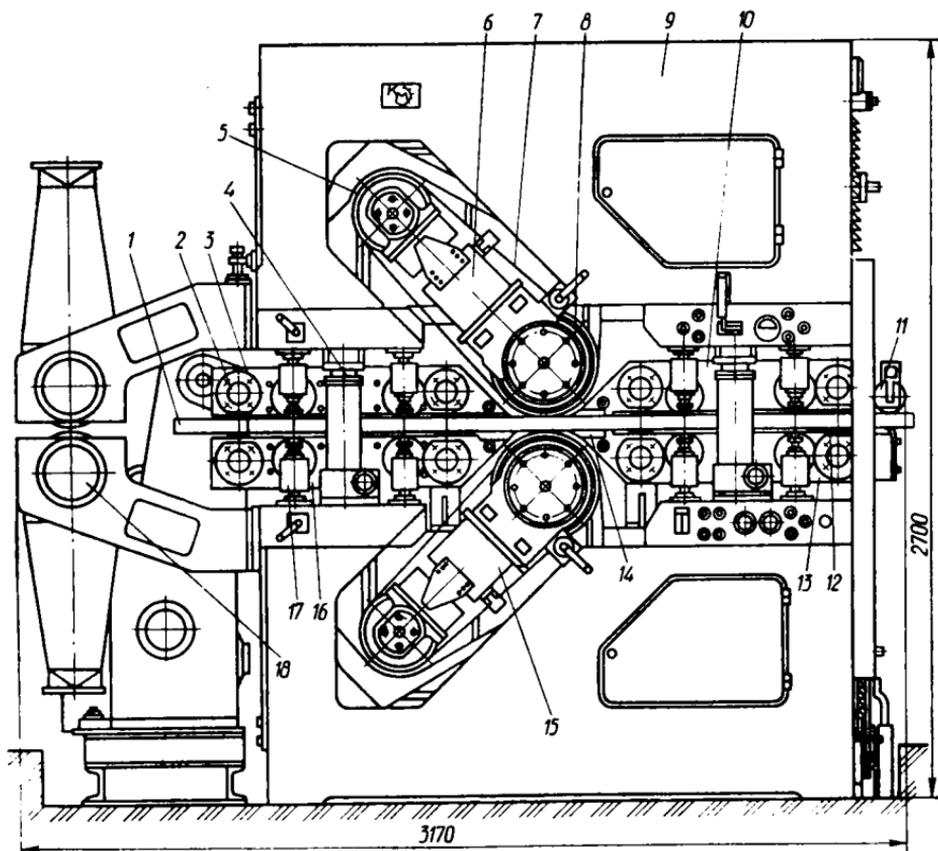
Калибровально-шлифовальный станок ДКШ-1:
